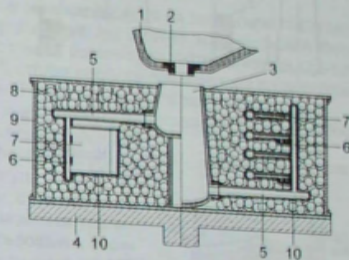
Схема типового металлопровода для центробежной заливки формы
